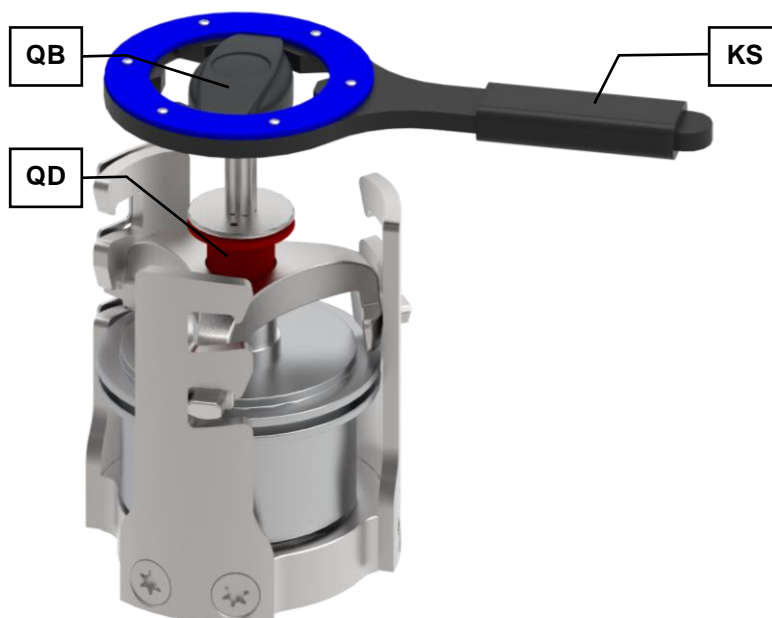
Impiego dell'ausilio di apertura per unità di serraggio
